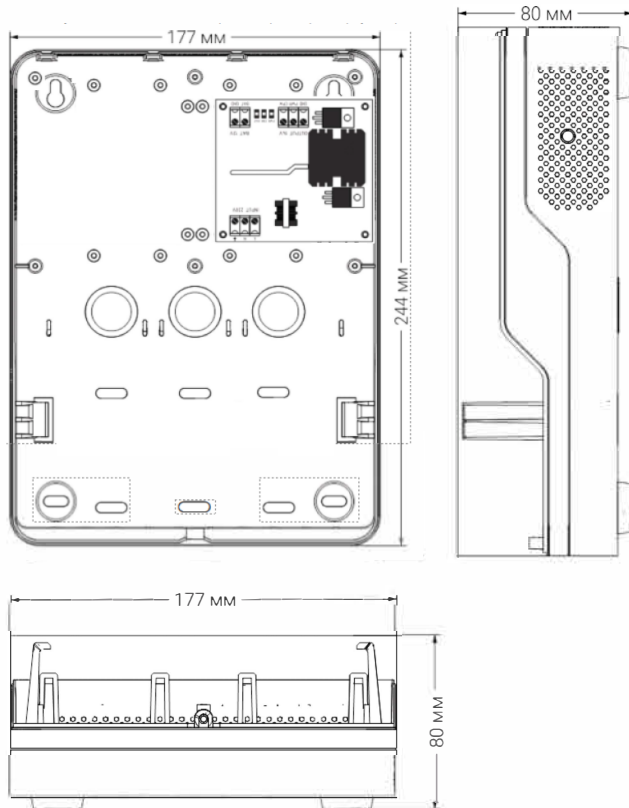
Корпус BigBox3 под АКБ 7Ач
